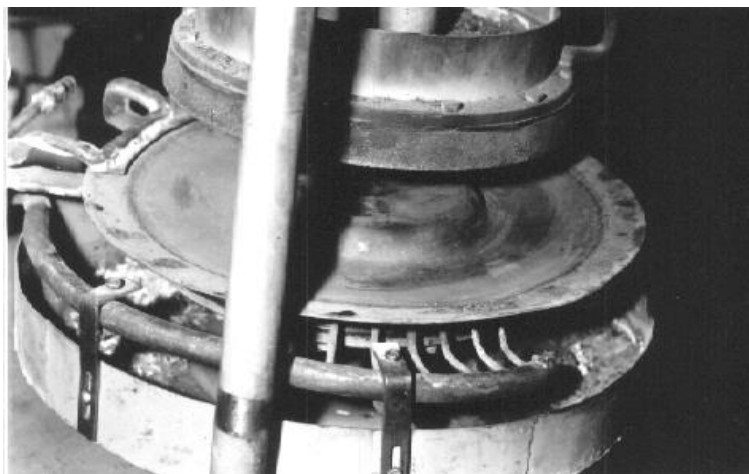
Пристрій для наплавлення цільноштампованого суцільного ножа за допомогою сегментного індуктора [2]
